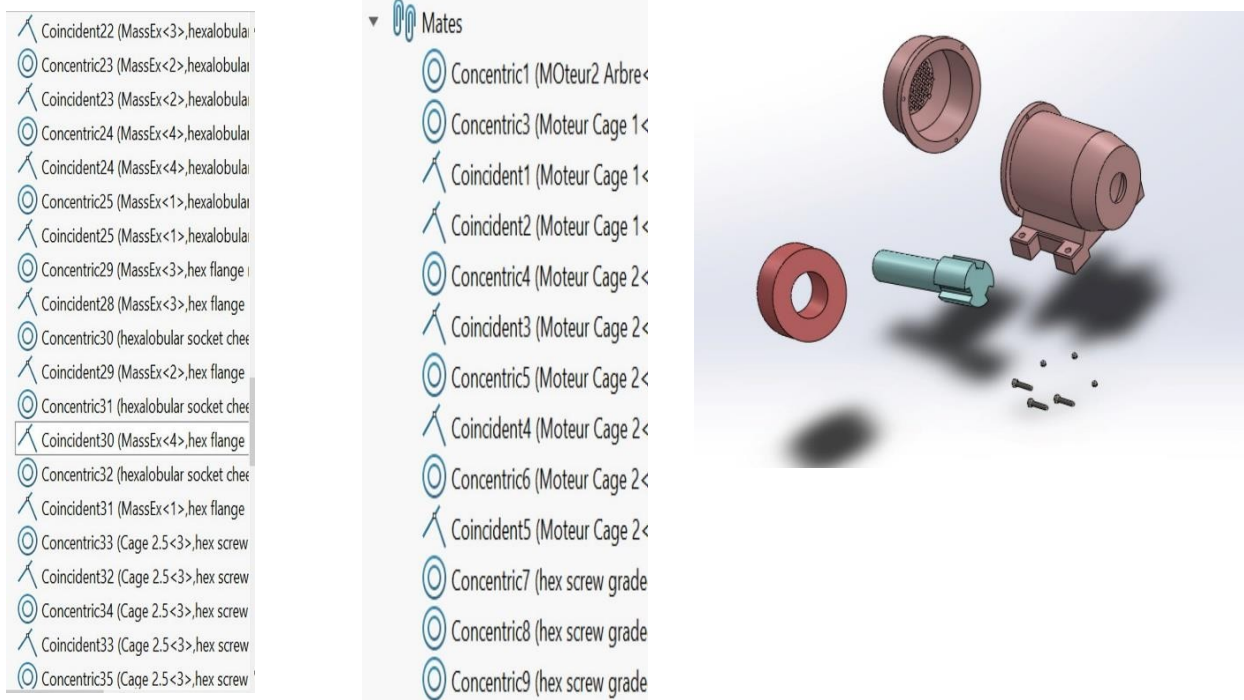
Les composantes du sous assemblage 3 dans une seule zone graphique
